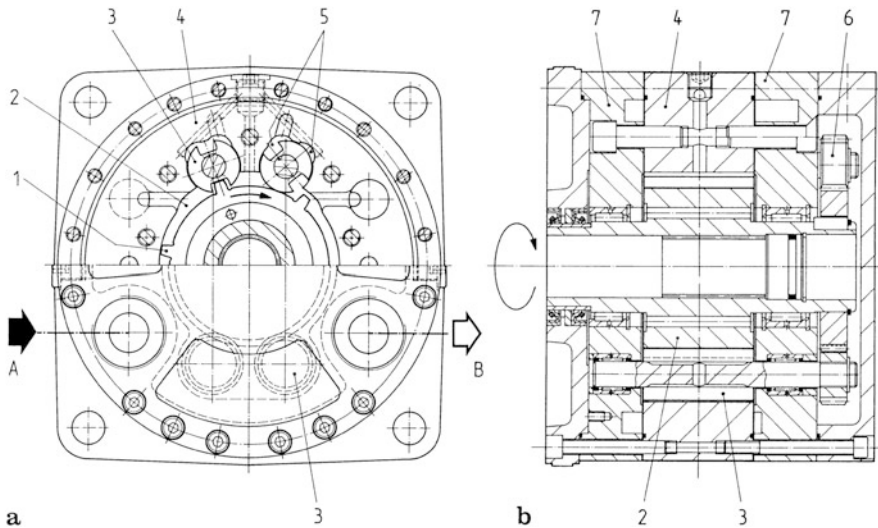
Rollflügelmotor (M 50, Rollstar). a Querschnitt mit paarweise gegenüberliegenden Dichtrotoren; b Längsquerschnitt mit Rotorsatz und läufergetriebener Steuerzahnradpaarung
